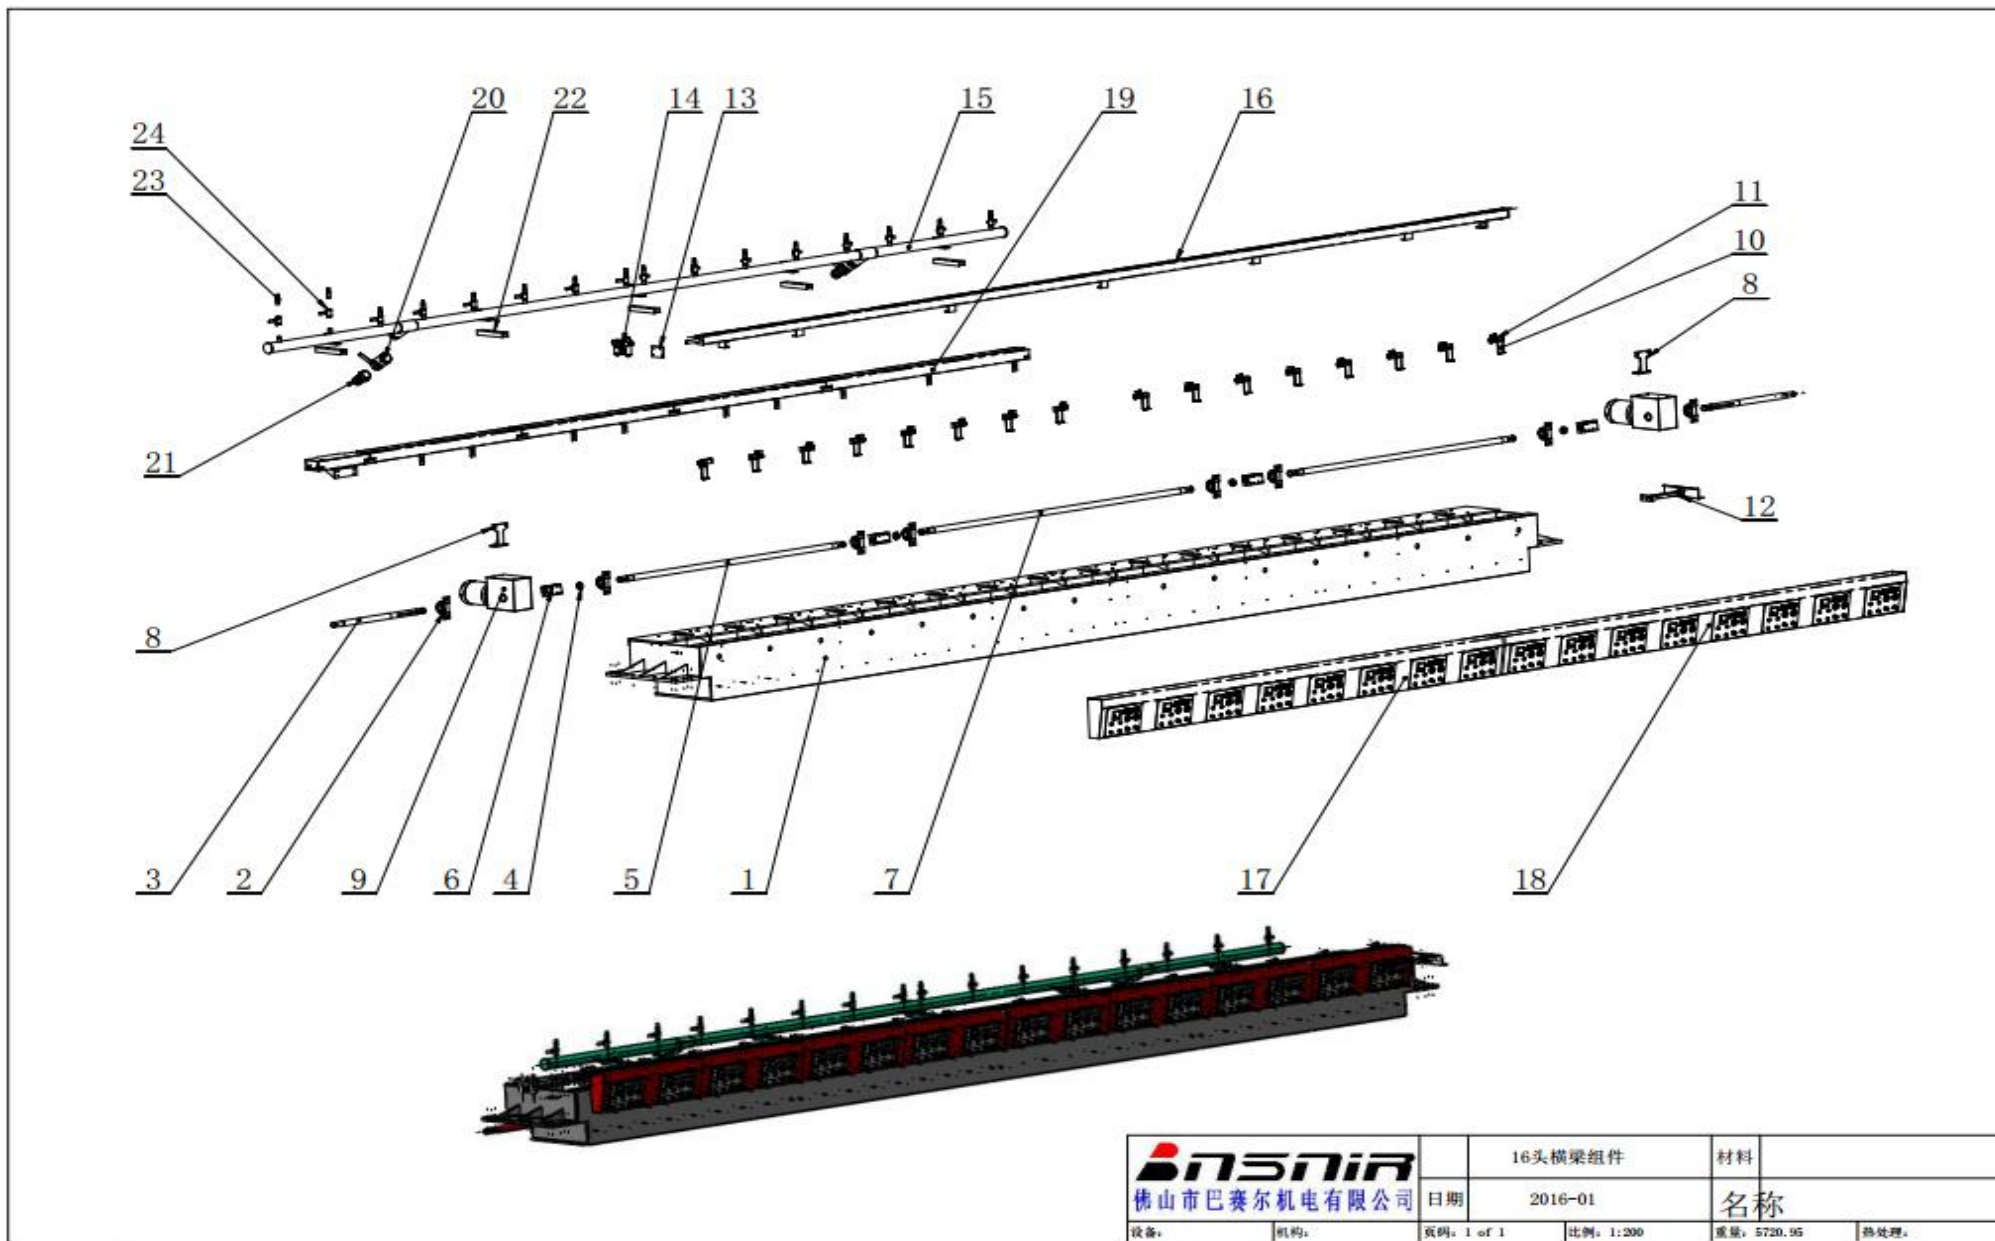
BP1000/16 抛光机——横梁组件装配图 picture 5 BP1000/16 polishing machine -- beam assembly drawing
